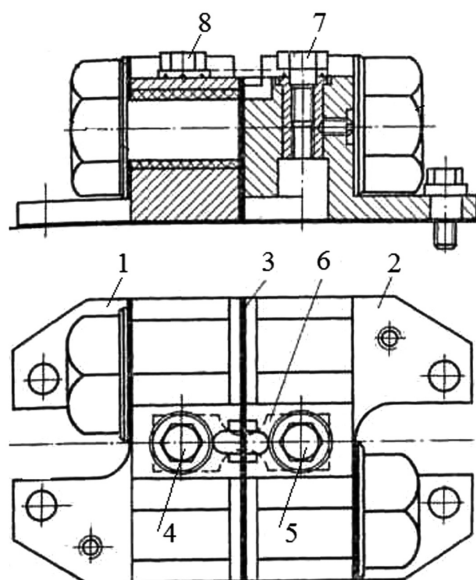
Блок нагружения установки для ТЦ испытания корсетных образцов: 1, 2 — жесткие опоры для закрепления и нагрева образца 6; 3 — прокладка электроизолирующая (слоуда); 4, 5 — левая и правая головки образца 6; 7, 8 — болты, фиксирующие головки образца в опорах 1, 2
